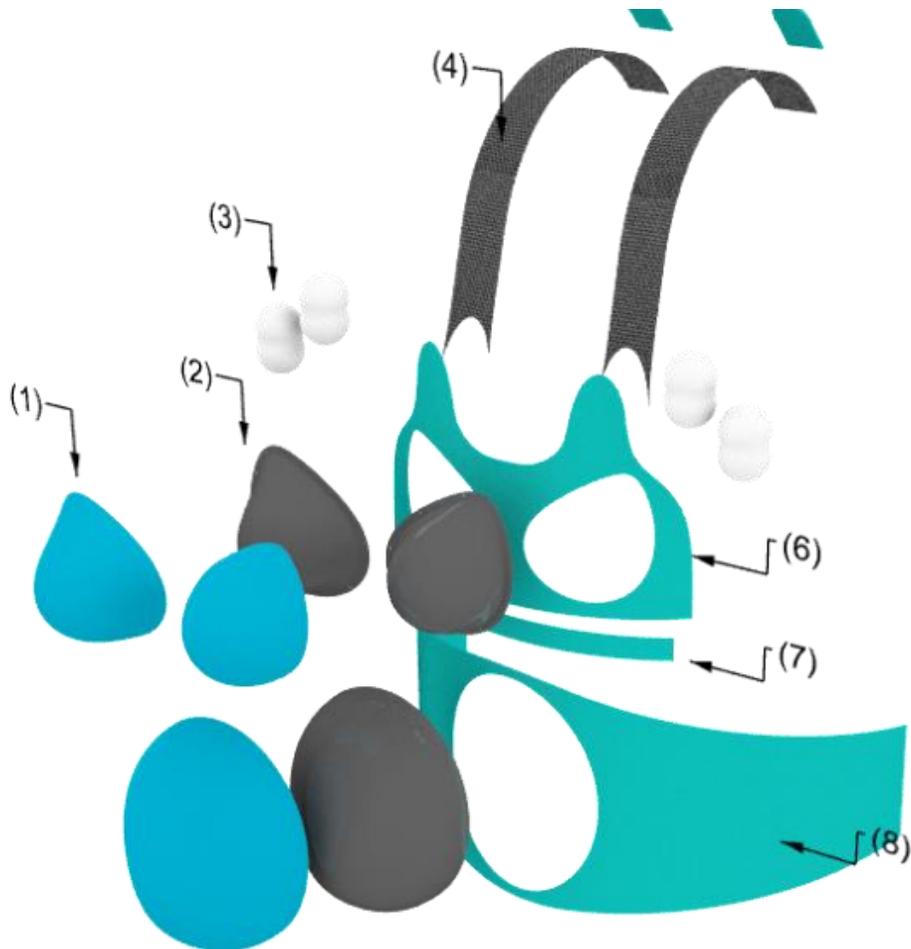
Explosión de Partes. Fuente: Desarrollo Propio.
